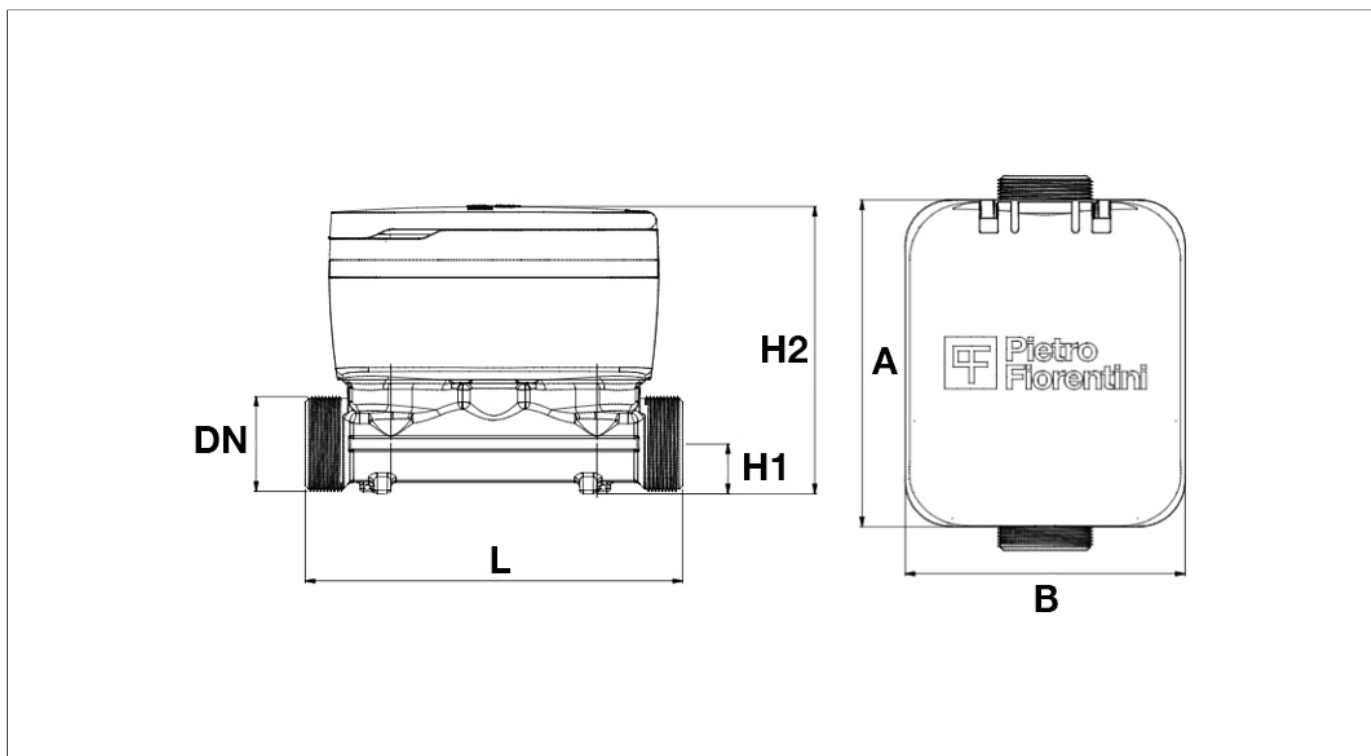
Dimensiones SSM-AQUO - versión en latón
